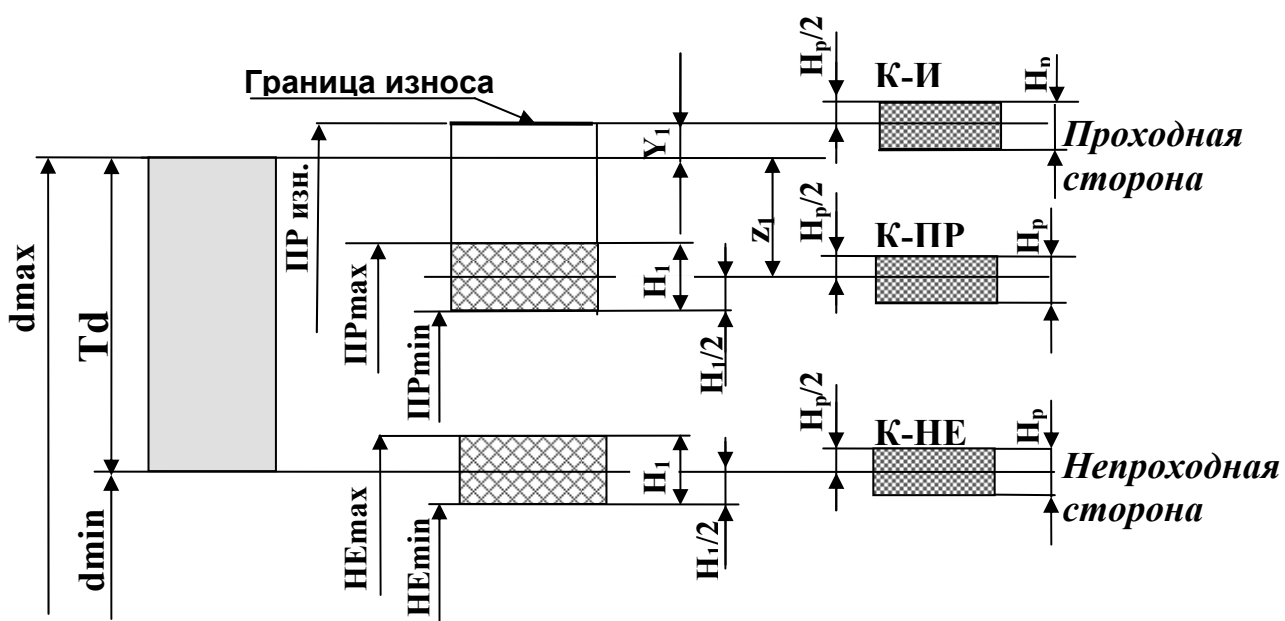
Контроль вала калибрами - скобами и контроль рабочих калибров-скоб контркалибрами
